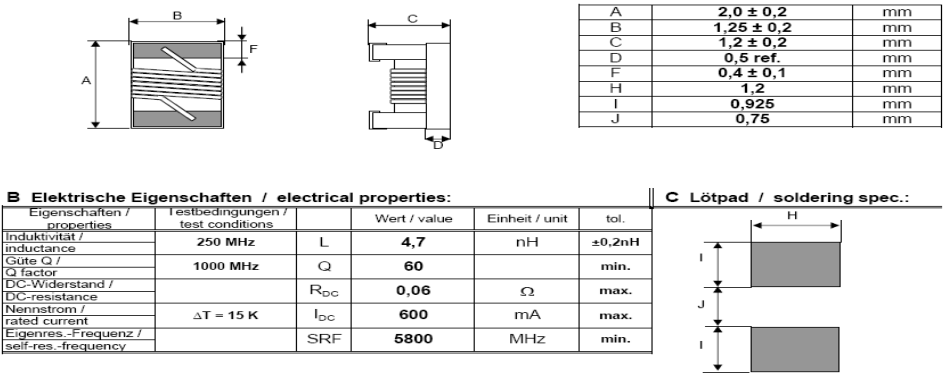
Dimensiones de las Bobina SMD encapsulado 0805.
